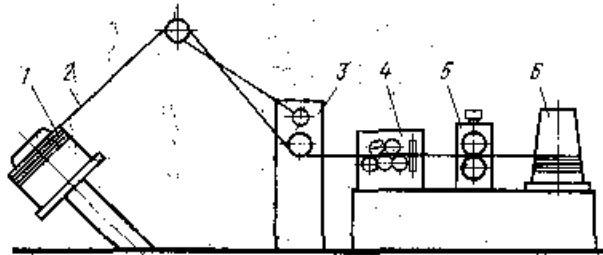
Волочильный стан для получения ромбической проволоки: 1— установочный барабан; 2 — проволока; 3 — устройство для аварийной остановки стана; 4 — правильное устройство; 5 — роликовая волока; 6 — приемный барабан
